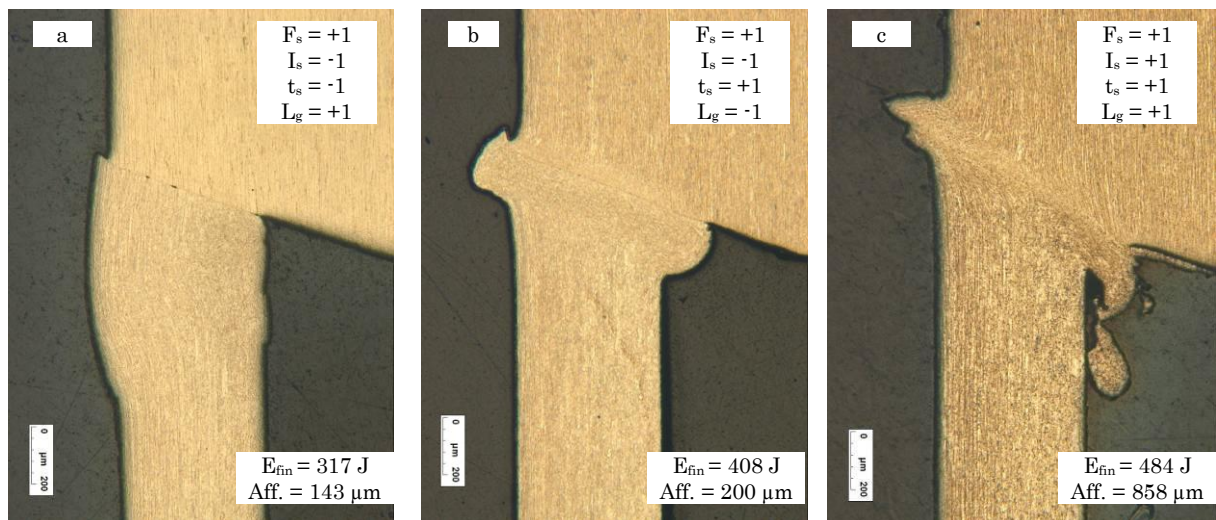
Macrographies typiques obtenues après attaque métallographique sur soudures en 9Cr-ODS
